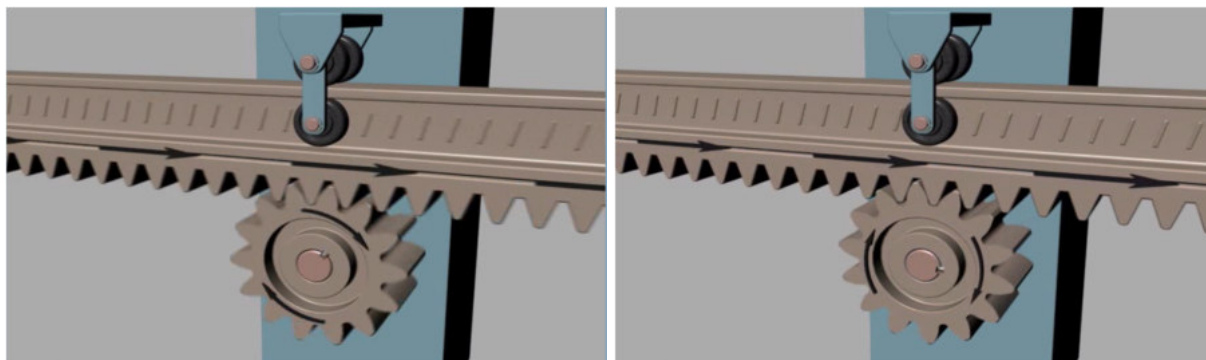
3D-модель рейкової передачі (рейка рухома)
